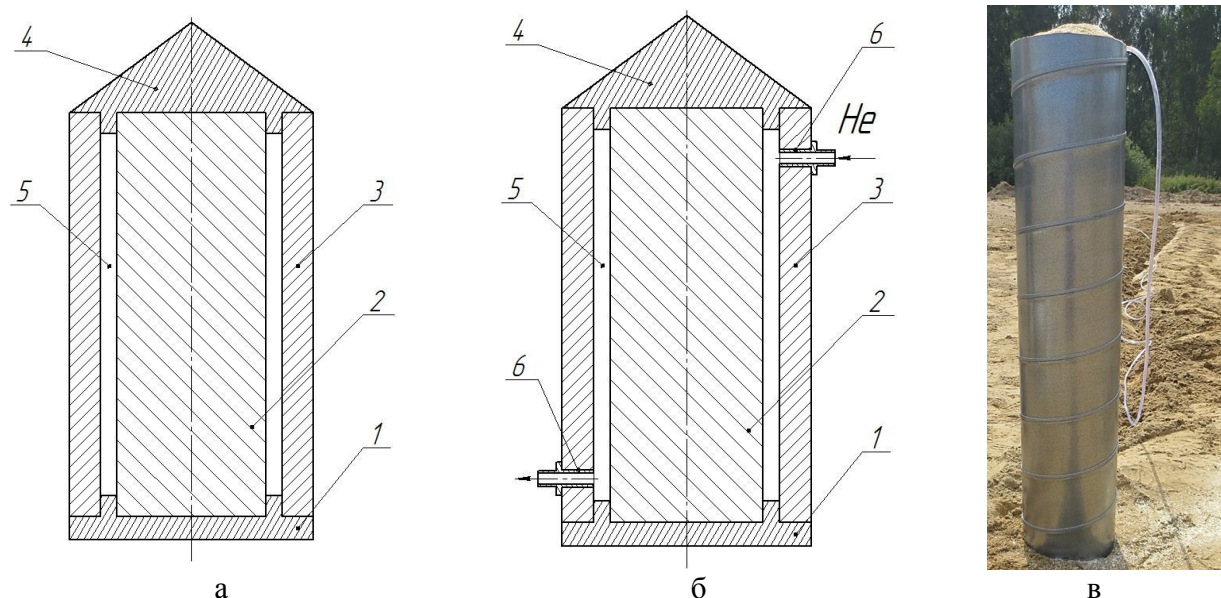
Схемы сборок исходных элементов под сварку взрывом: а – схема с использованием воздуха; б – схема с использованием гелия; в – сборка на полигоне
